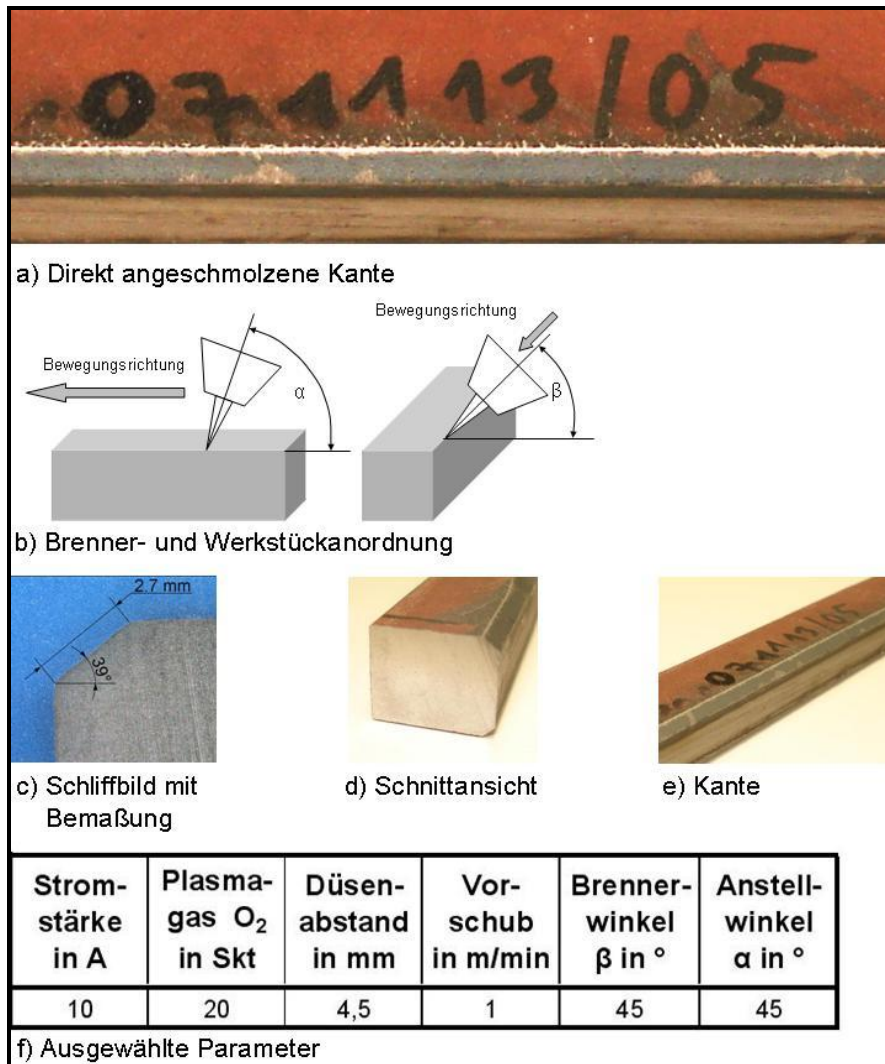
Mittels Plasmaschneidbrenner bearbeitete Kante
